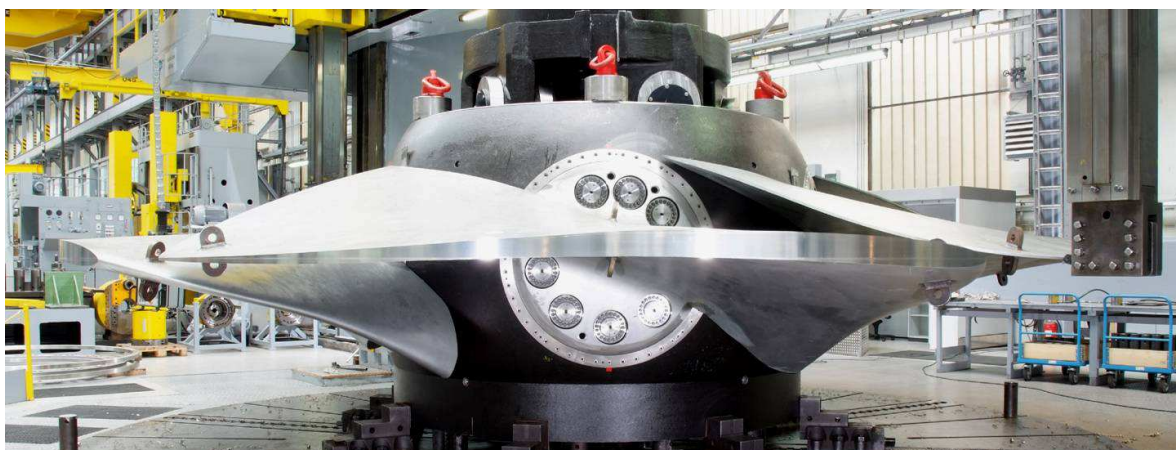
Foto da Fabricação de um Rotor Kaplan
